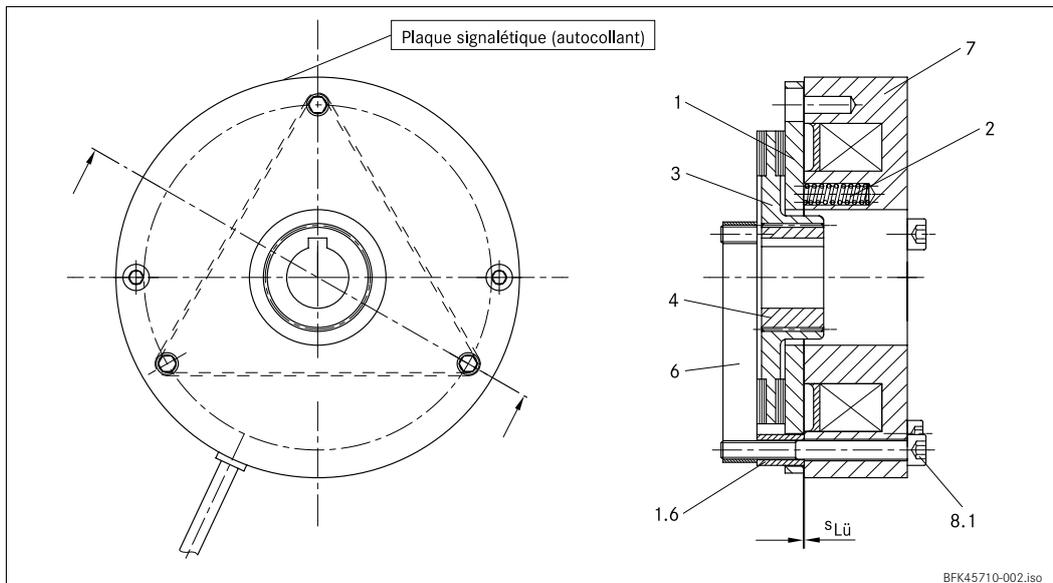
Structure du frein à ressorts à manque de courant BFK457-06...16 Basic, corps inducteur complet avec rotor
